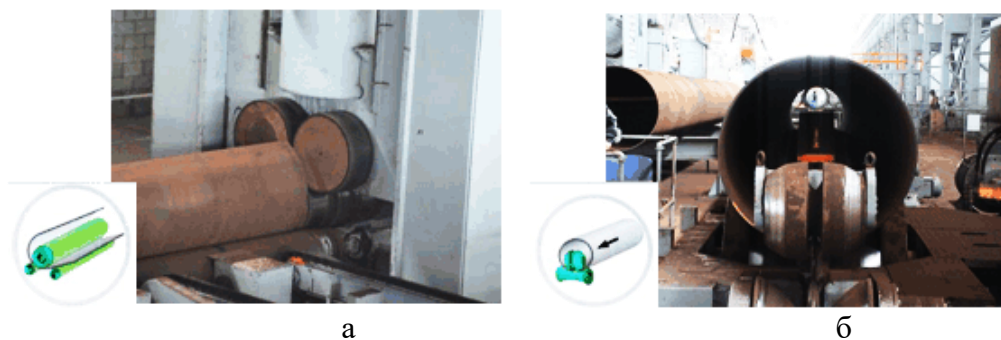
Формовки трубной заготовки: (а) на трех валковой листогибочной машине, и (б) доформовка кромок трубной заготовки.
